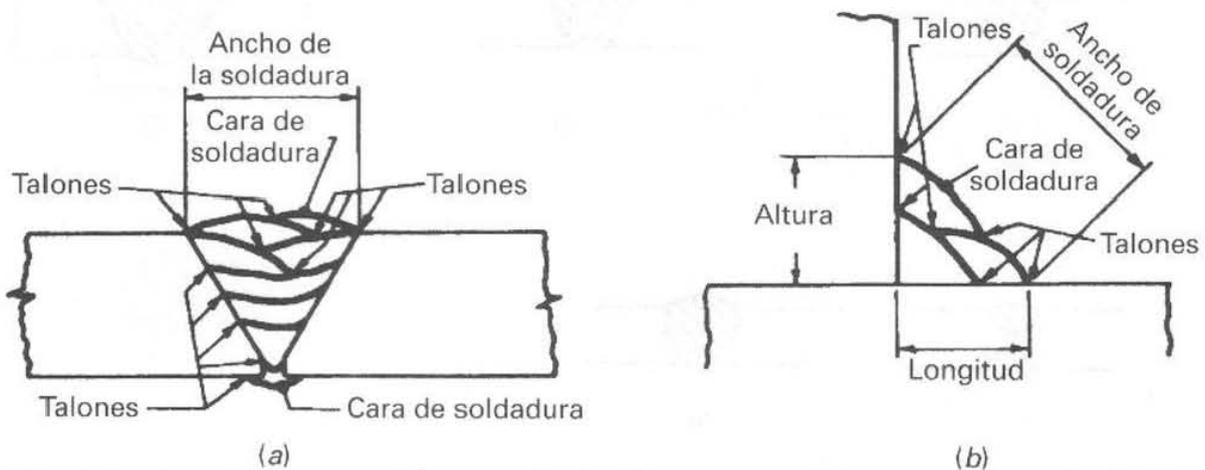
Terminología de la soldadura para soldadura a tope y con material de relleno. (a) Detalles descriptivos de la soldadura a tope. (b) Detalles descriptivos de la soldadura por puntos.
